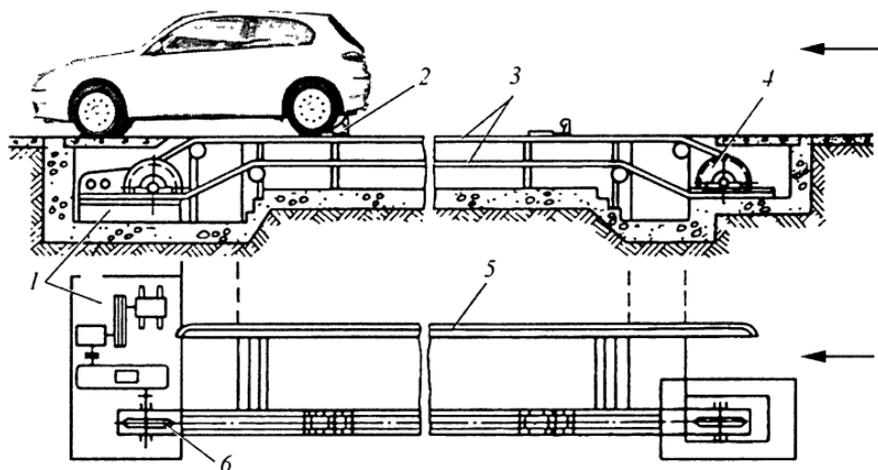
Толкающий конвейер: 1 — приводная станция; 2 — толкающая тележка; 3 — цепи; 4 — натяжная станция; 5 — направляющая; 6 — звездочка
